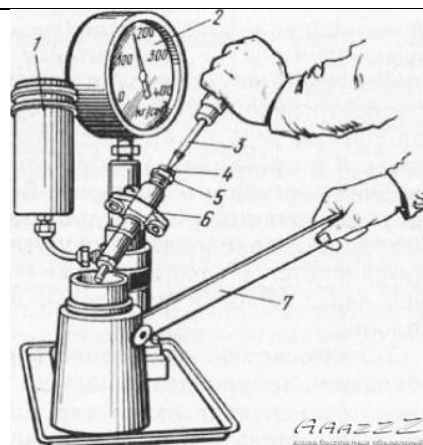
Стенд для регулировки форсунок дизельного двигателя.
